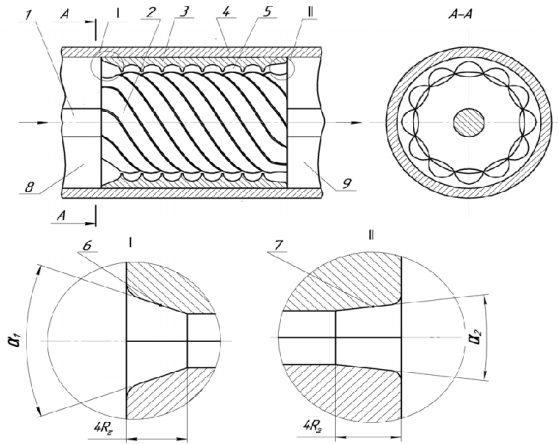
Удосконалені робочі органи насоса [7]: 1 – привідний вал; 2 – гвинт; 3 – втулка; 4 – корпус; 5 – гвинтова канавка; 6 – вхід в робочу зону ЛГН; 7 – вихід з робочої зони ЛГН; 8 – камера підводу; 9 – камера відводу.
